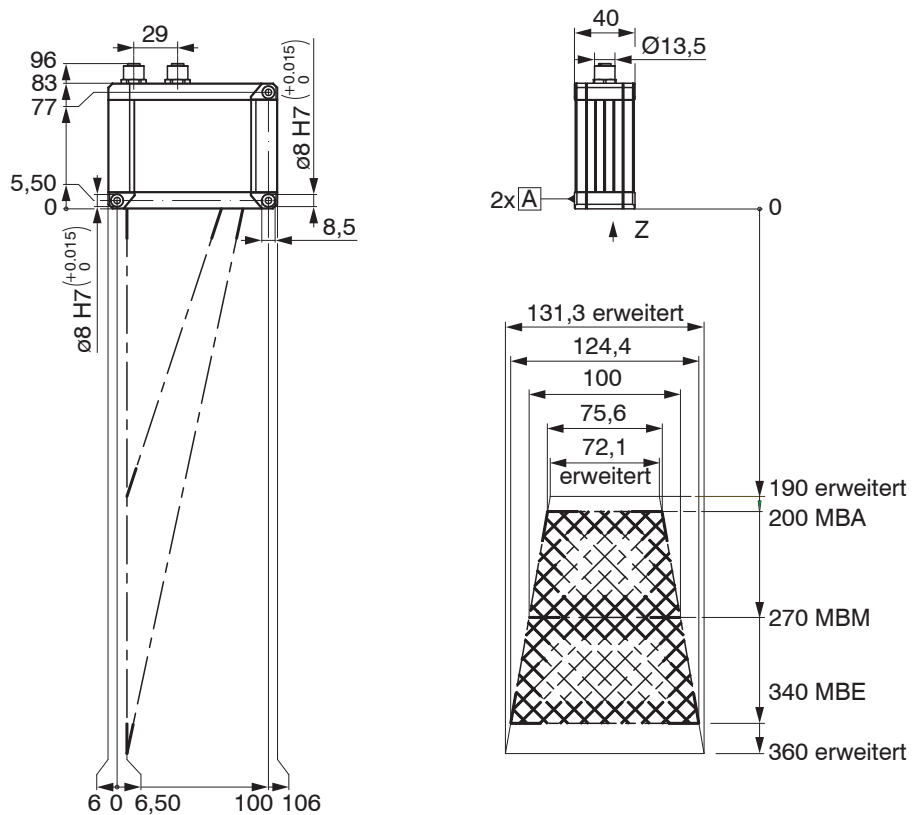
Maßzeichnung Sensor scanCONTROL 30xx-100
